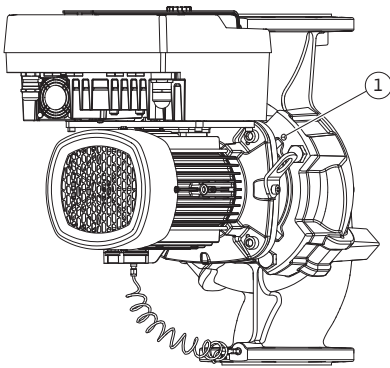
Abdrücken des Einstecksatzes über Gewindebohrungen (je nach Pumpentyp)
